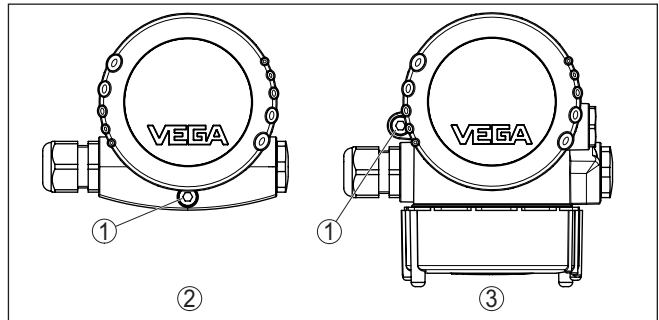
Position der Sicherungsschraube je nach Gehäuse
